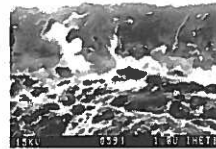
Superfície de fractura: aspectos de iniciação
